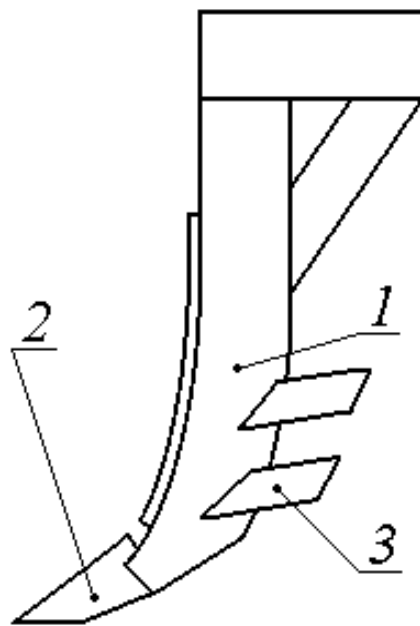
Конструктивна схема чизеля - розпушувача RZ-220.7:
